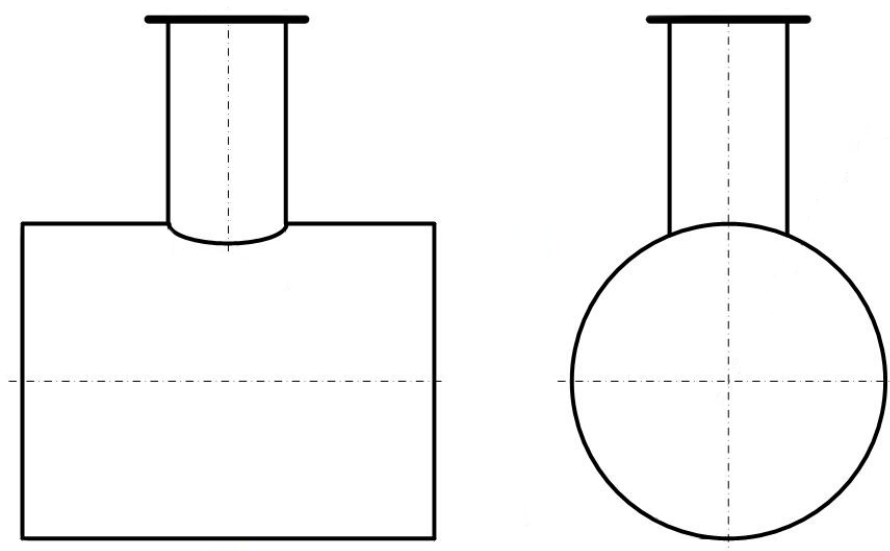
Общий вид эскиза резервуара РГС-10
